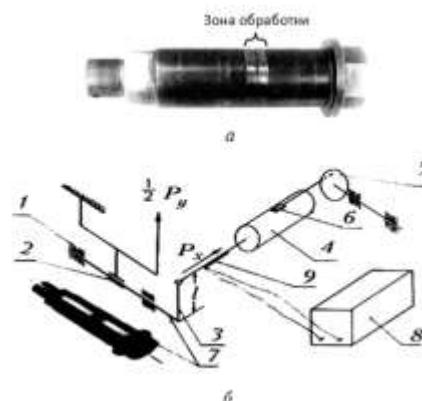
Внешний вид болта (а) и схема стенда для макетных испытаний шарнирно-болтовых соединений (б):
